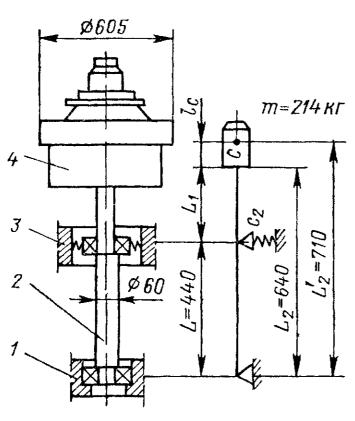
Ротор сепаратора и расчетная схема его консольного вала с податливой опорой 1 — подшипник; 2 — вал; 3 — упругая опора, 4 — барабан
